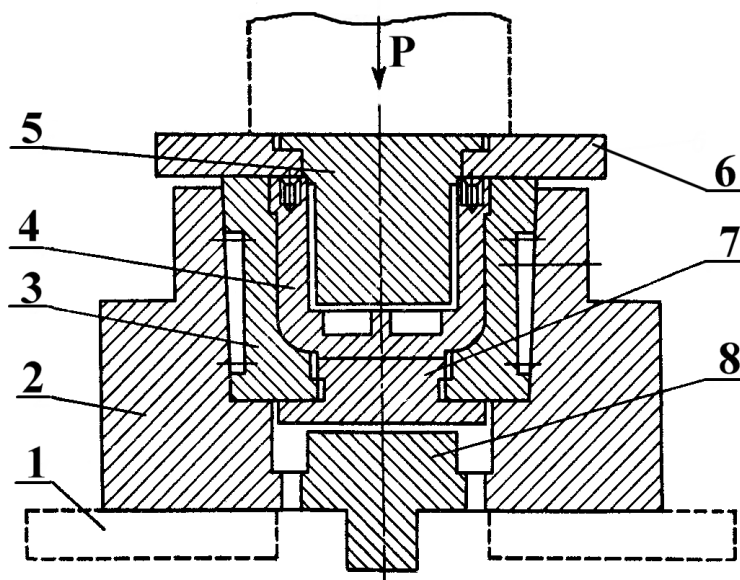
Приспособление для обжатия корпусов насосов:
